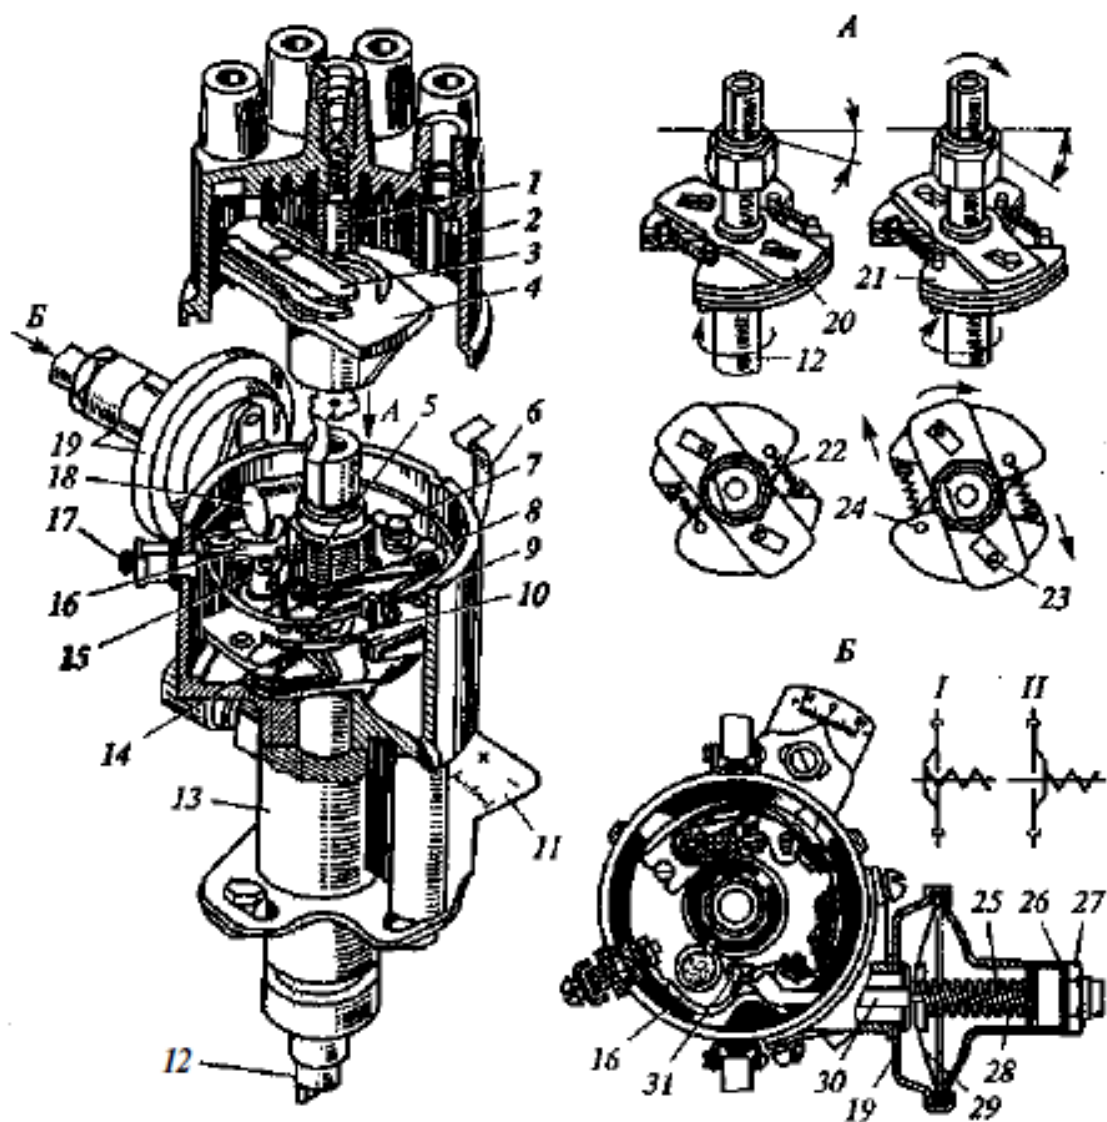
Прерыватель-распределитель классической контактной системы зажигания: 1 – угольный электрод; 2 – крышка; 3 – токоразносная пластина; 4 – ротор (бегунок); 5 – кулачок; 6 – защелки крышки; 7 – эксцентрик (регулирующий винт); 8 – подвижный контакт прерывателя; 9 – контактная стойка; 10 – опорная пластина контактной группы; 11 — шкала настройки угла опережения зажигания; 12 – вал привода кулачка; 13 – корпус; 14 – стопорный винт; 15 – проводник к контактной группе; 16 – опорный диск; 17 – контактный винт; 18 – конденсатор; 19 – корпус вакуумного регулятора опережения зажигания; 20 – ведущая пластина (траверса); 21 – грузики; 22 – стяжная пружина; 23 – штифт грузика; 24 – ось вращения грузиков; 25 – крышка вакуумного регулятора; 26 – прокладка; 27 – штуцер; 28 – пружина; 29 – диафрагма; 30 – тяга; 31 – штифт для тяги; А – центробежный регулятор; Б – вакуумный регулятор; I и II – положения диафрагмы
